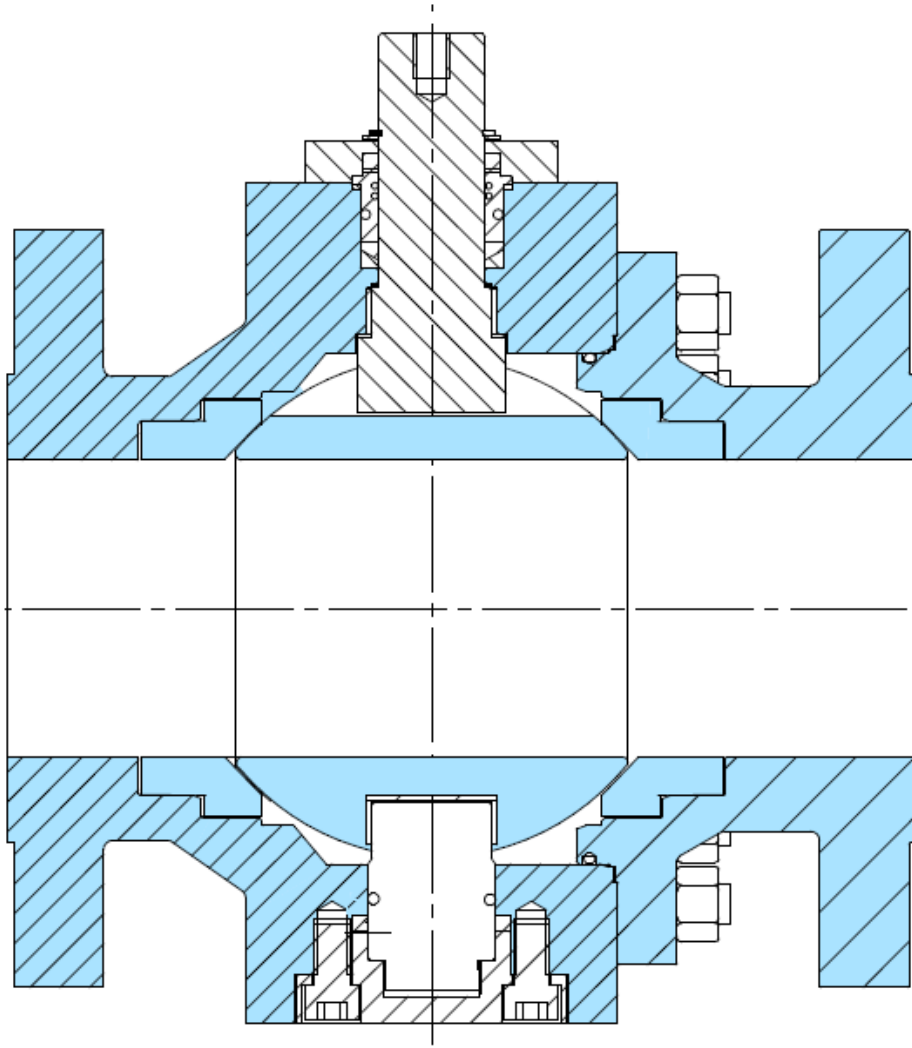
Parts d'una vàlvula de bola en contacte amb el fluid (en blau)
